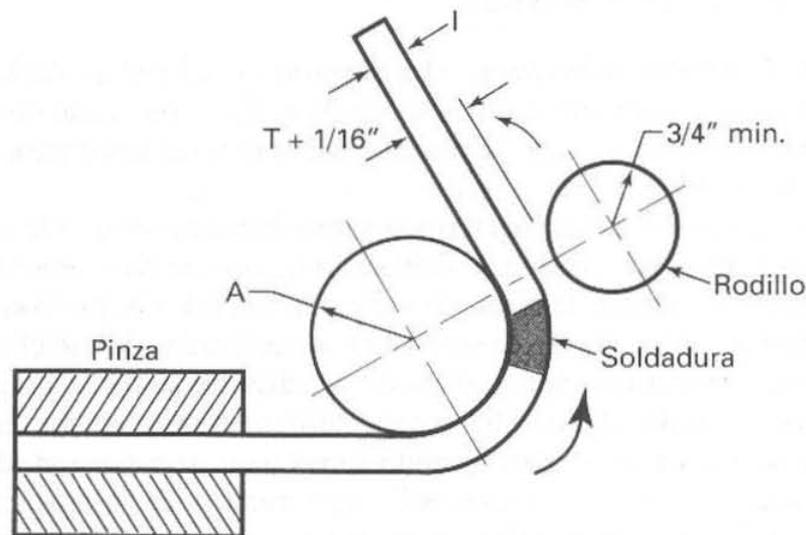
Las pruebas mecánicas de soldadura incluyen flexión guiada de las soldaduras de garganta. La ilustración es de la prueba de doblado de cara.
